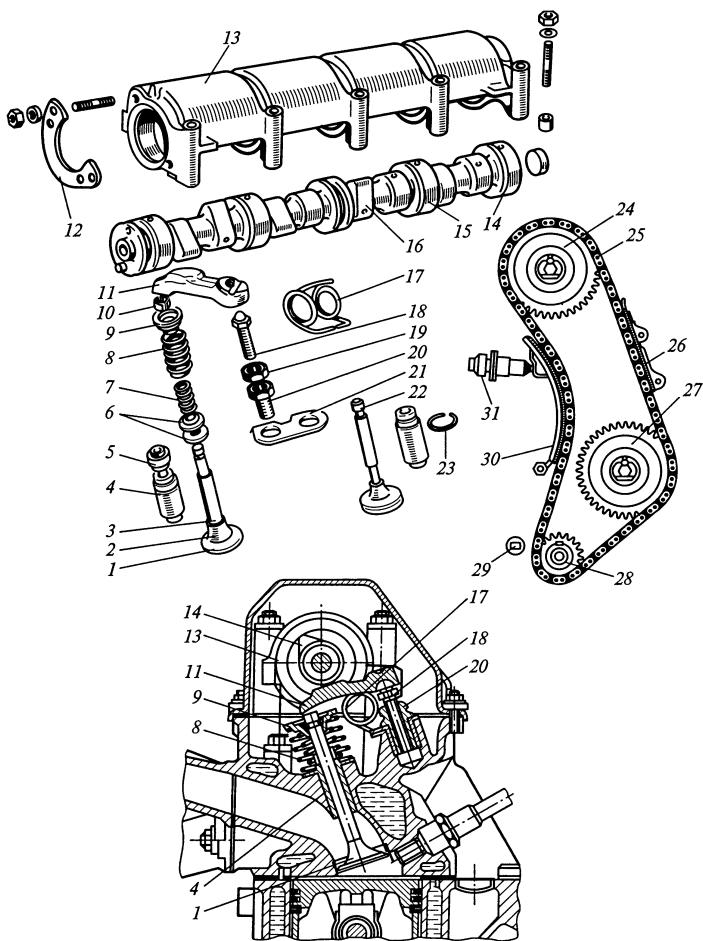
Газораспределительный механизм двигателей легковых автомобилей ВАЗ-2105:
